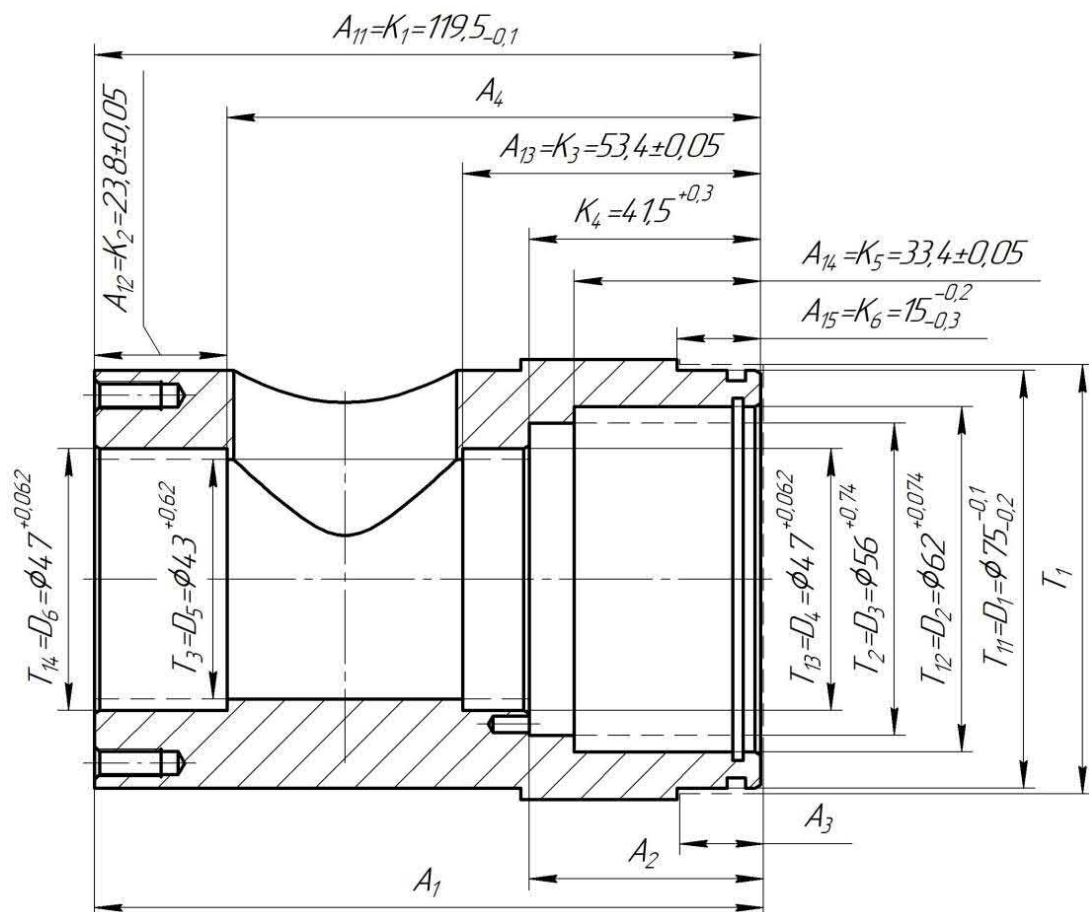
Размерная схема токарной операции с ЧПУ (045)
